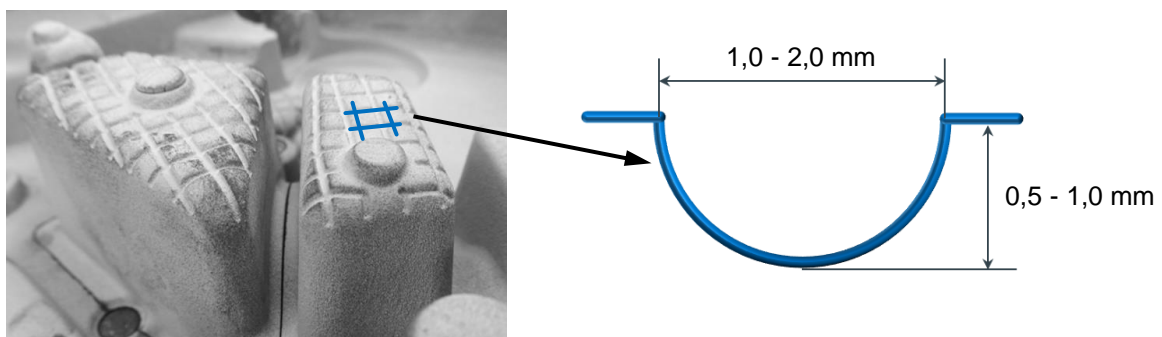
Kokille mit Oberflächenstruktur (links) und schematischer Strukturdarstellung (rechts) [140]
